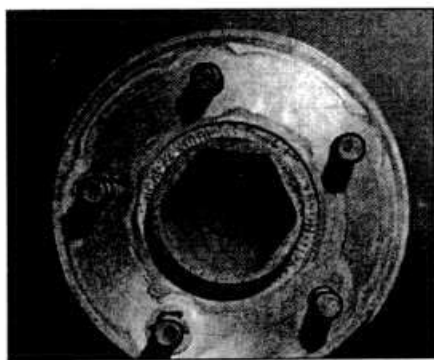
Стопорное кольцо диска тормозного механизма переднего колеса
